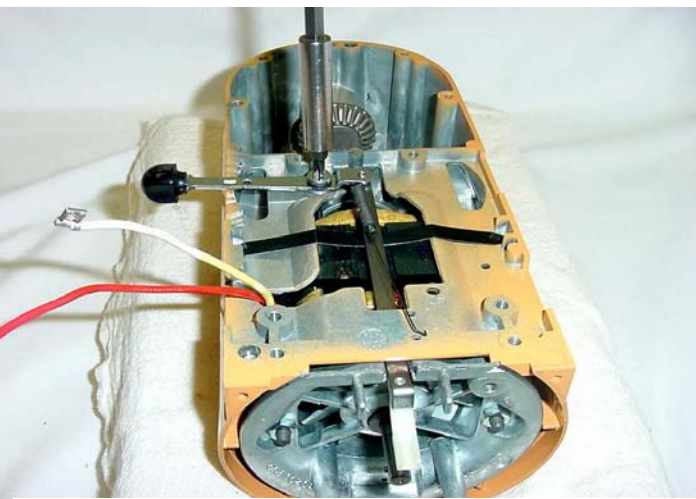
Drehpunktschraube nach Aufsetzen der Spannscheibe befestigen.
